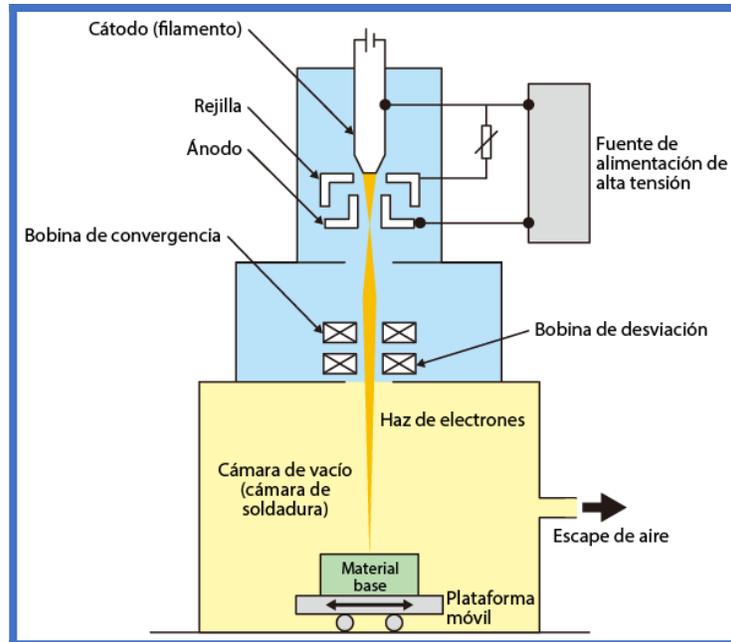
Representación del equipo de soldadura por haz de electrones.
